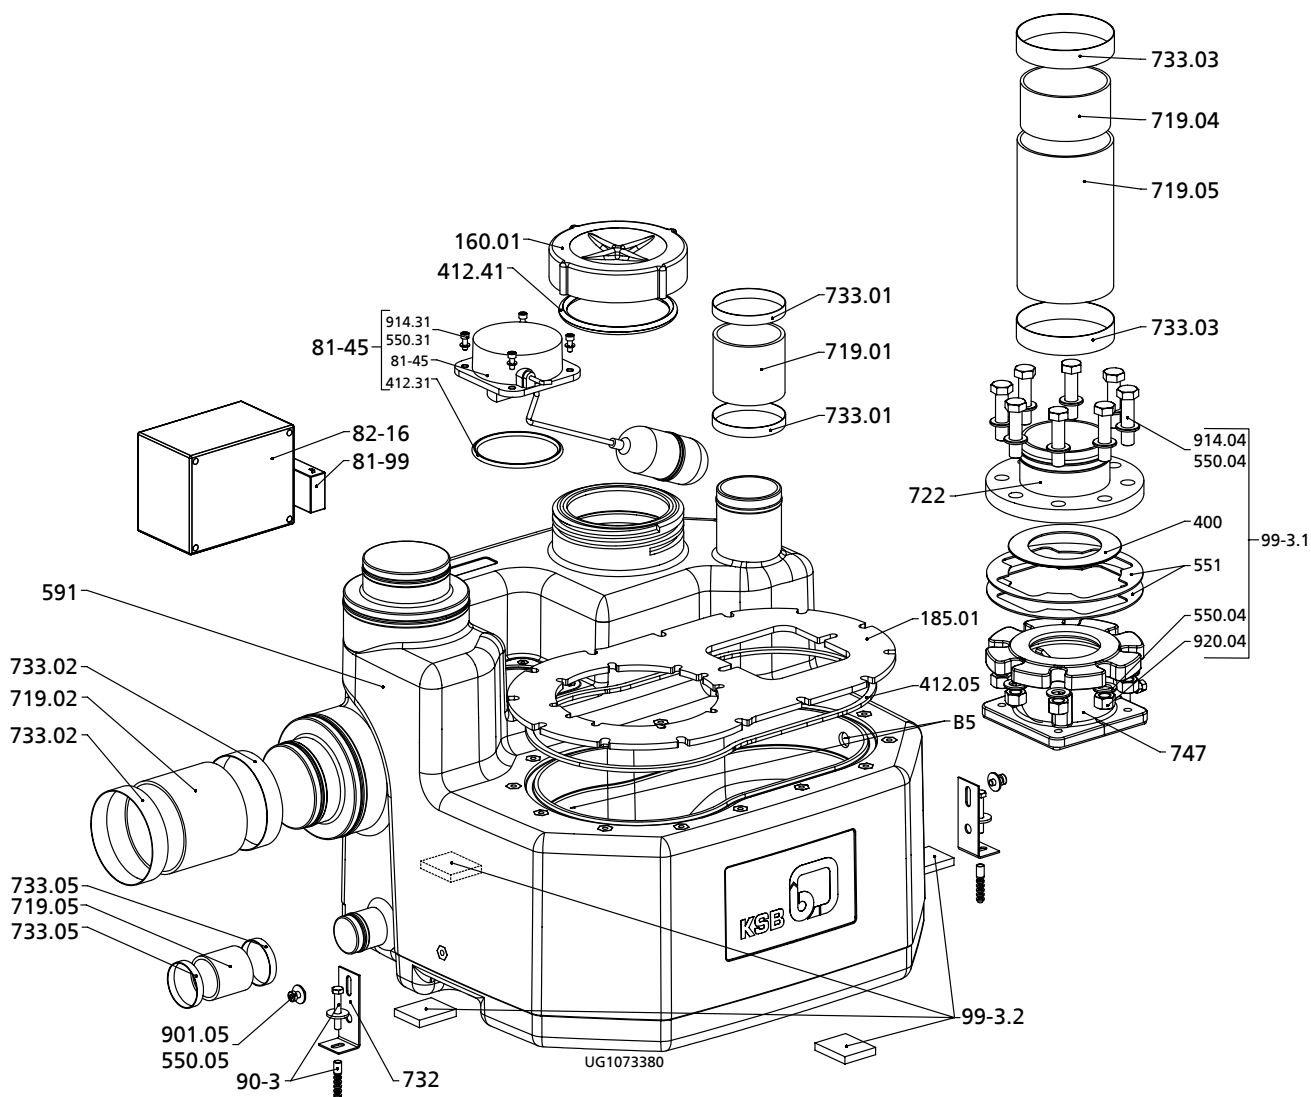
Покомпонентный сборочный чертеж Compacta U100 – резервуар
